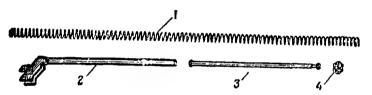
Возвратный механизм: 1 — возвратная пружина: 2 — направляющий стержень; 3 — подвижный стержень; 4 — муфта
